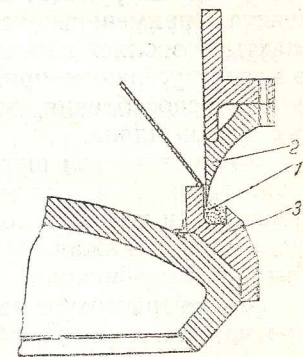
Схема уплотнения нижнего конуса загрузочной коробки: 1 — гнездо с торфяной крошкой и пылью; 2 — надставная часть корпуса коробки (разъемное кольцо); 3 — надставная часть тарелки (разъемное кольцо).
